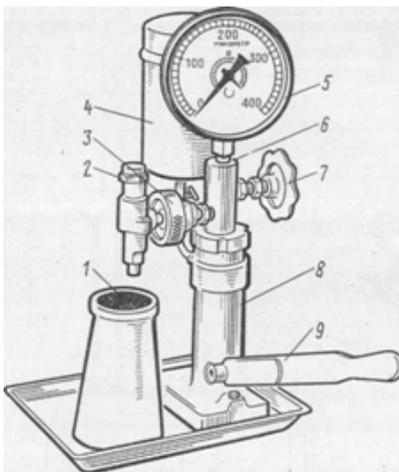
Прибор КП-1609А для проверки и регулировки форсунок: 1 — прозрачный сборник топлива, 2 — форсунка, 3 — маховичок крепления форсунки, 4 — бачок, 5 — манометр, 6 — корпус распределителя, 7 — запорный кран, 8 — плунжерный насос, 9 — рычаг привода насоса
